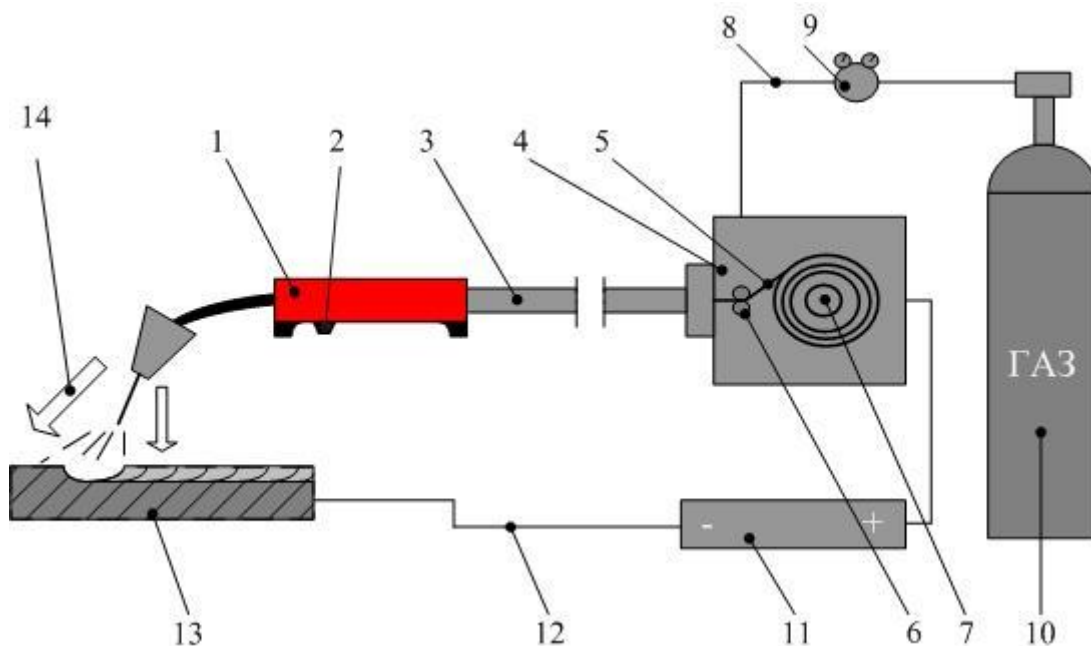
Схема полуавтомата включает: 1 - сварочную горелку с держателем пистолетного типа; 2 - клавишу «пуск»; 3 - гибкий шланг: с проходящими цепями управления, с кабелем, подводящим ток к контактному мундштуку внутри сопла горелки, с трубкой для прохода сварочной проволоки; 4 - проволочноподающий механизм состоит из: сварочной проволоки - 5, подаваемой к месту сварки с помощью роликов - 6, толкающих проволоку к соплу горелки из бухты - 7; 8 – шланг для подвода защитного газа из баллона - 10 через редуктор - 9 в горелку; 11 - сварочный выпрямитель с кабелями -12 для подвода тока к изделию -13; 14 – струя защитного газа, вытесняющая воздух из зоны плавления и кристаллизации металла шва.
